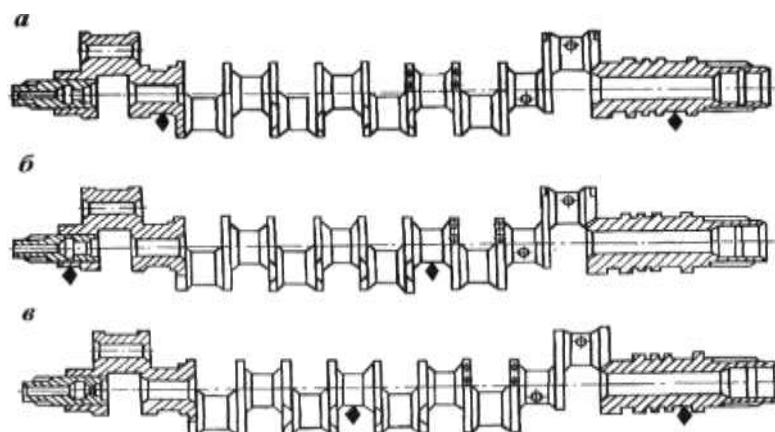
Схема правки колінчастого вала: а - правка корінних шийок вала;
